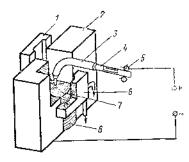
Схема сварки порощковой проволокой с принудательным формированием сварпого шва
